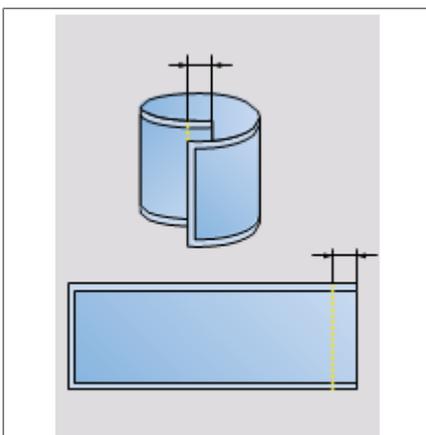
Franja solapada en el caso de máquina izquierda-derecha
